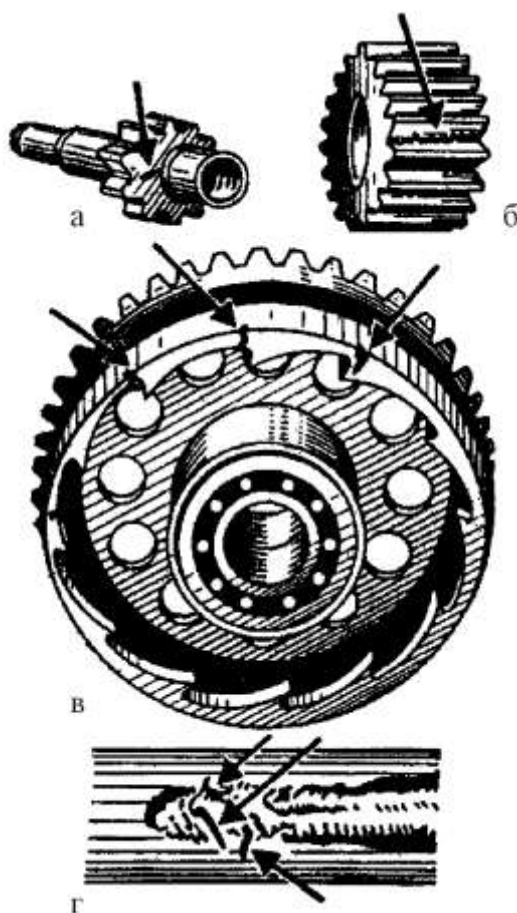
Дефекти деталей, виявлені магнетопорошковим методом: а, б – утомні тріщини на шестернях; в – тріщини гартувальні; г – тріщини в зваровому шві
